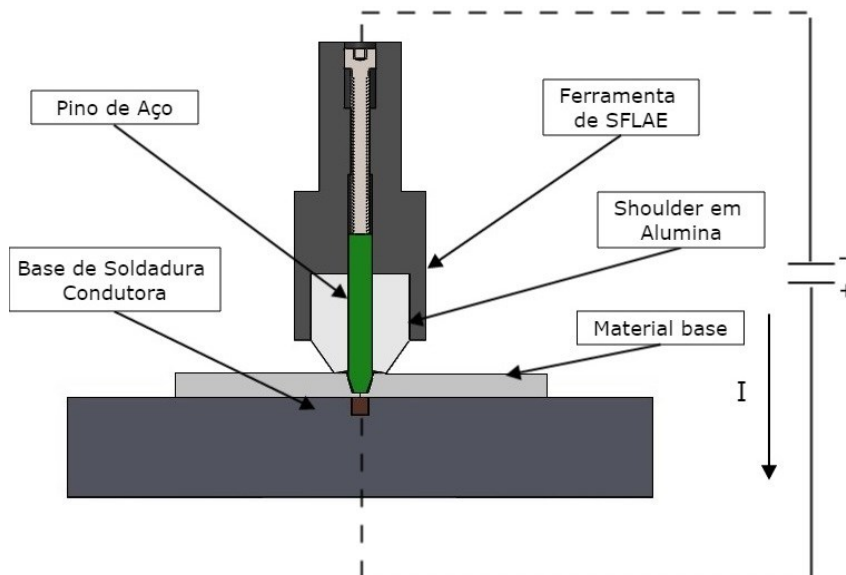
Esquema de soldadura por fricção linear assistida por corrente elétrica para a abordagem tecnológica #2.
